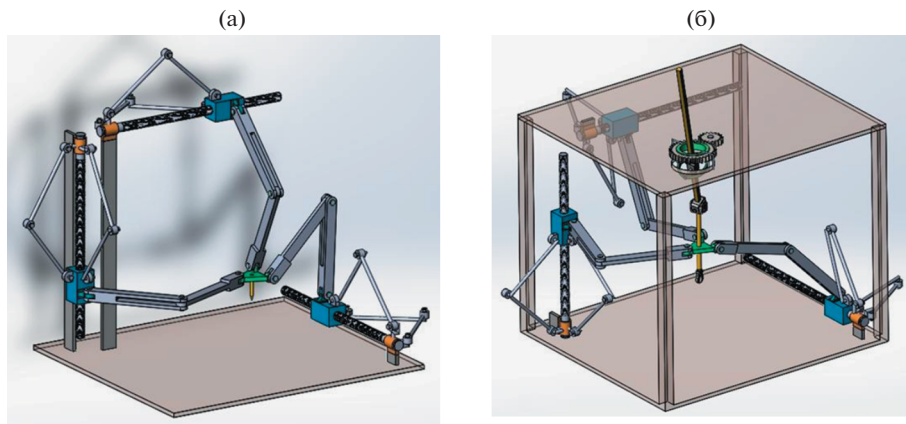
Механизм с тремя вращательными приводами, снабженный структурными группами Ассура: (а) – без дополнительной кинематической цепи; (б) – с дополнительной кинематической цепью.
